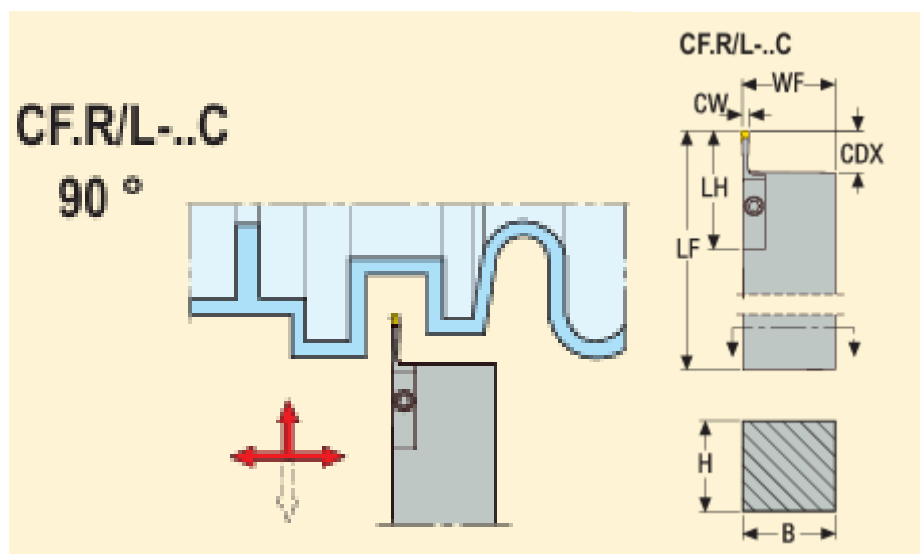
Державка CFOL3244M-0317C [1, с. 719]
